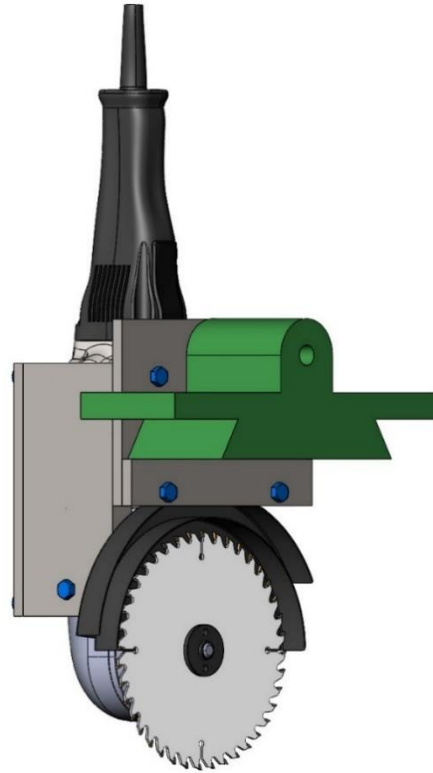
3-D модель высокоскоростной фрезерной головки
